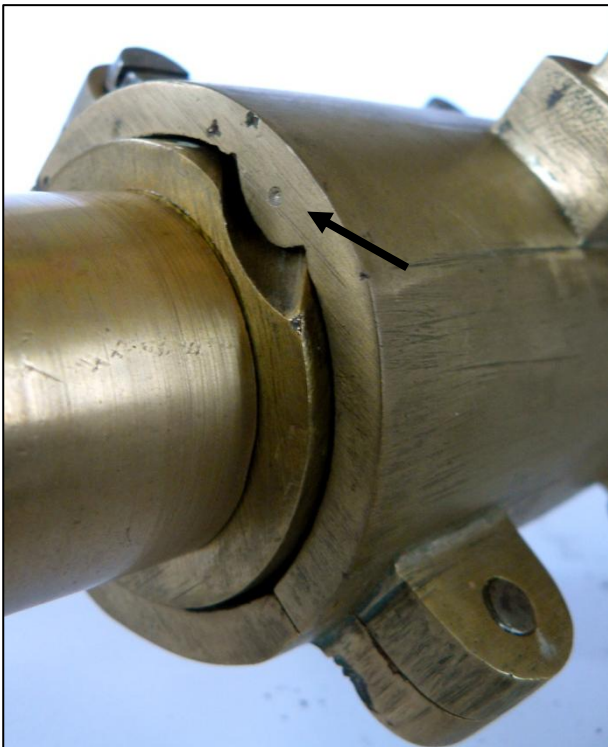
Spindel med spiralelement nr. 3957 (detalje)
